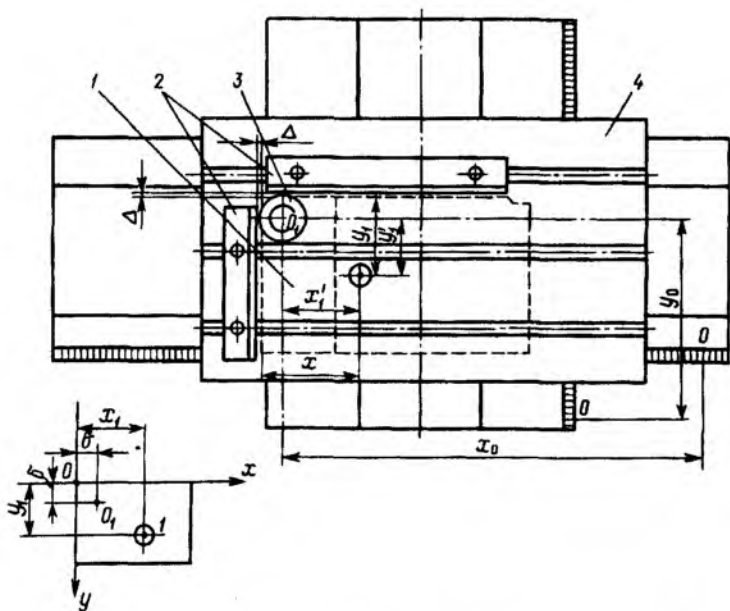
Установка стола сверлильного станка в исходное положение: 1 — деталь, 2 — планки, 3 — оправка, 4 — стол
